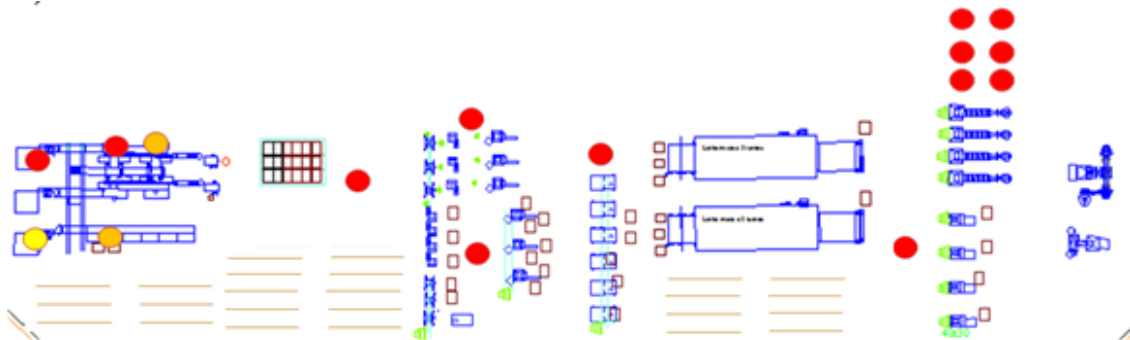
Layout linha mista e pessoas alocadas à produção
